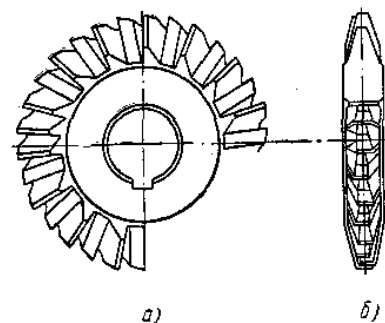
Дисксовая резьбовая фреза (а), контрольный зуб (б)
